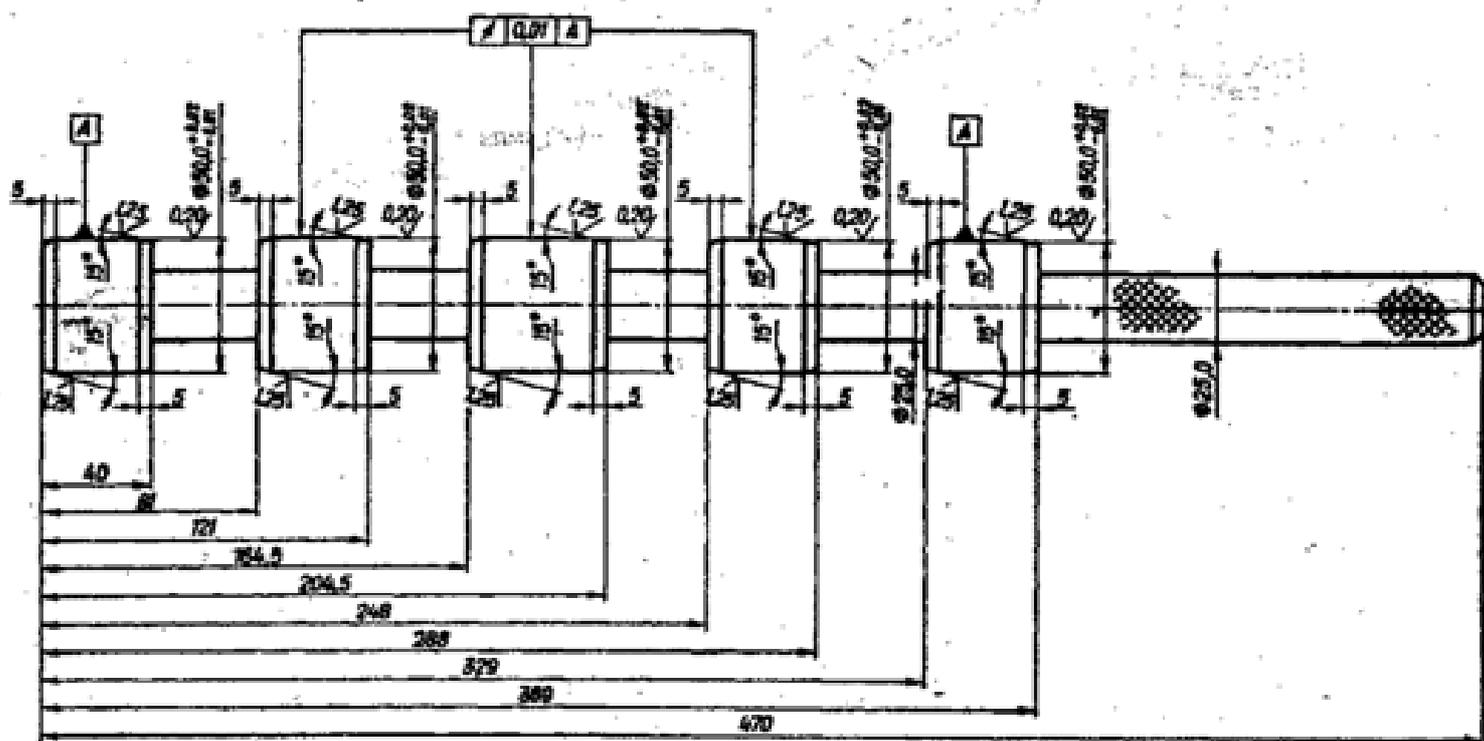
Оправка для проверки соосности коренных подшипников коленчатого вала
